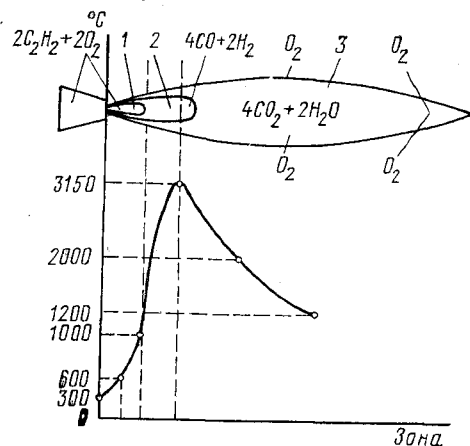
Схема строения сварочного нейтрального пламени:
